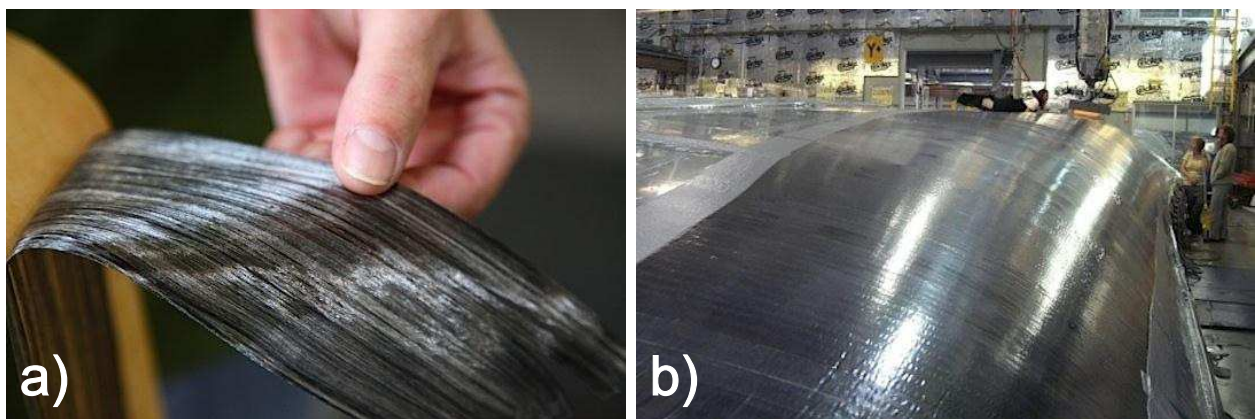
a. Bandelette qui constitue les panneaux de 3Di. b. Fabrication d'une voile 3Di par assemblage de panneaux (images issue du site www.northsail.com).
